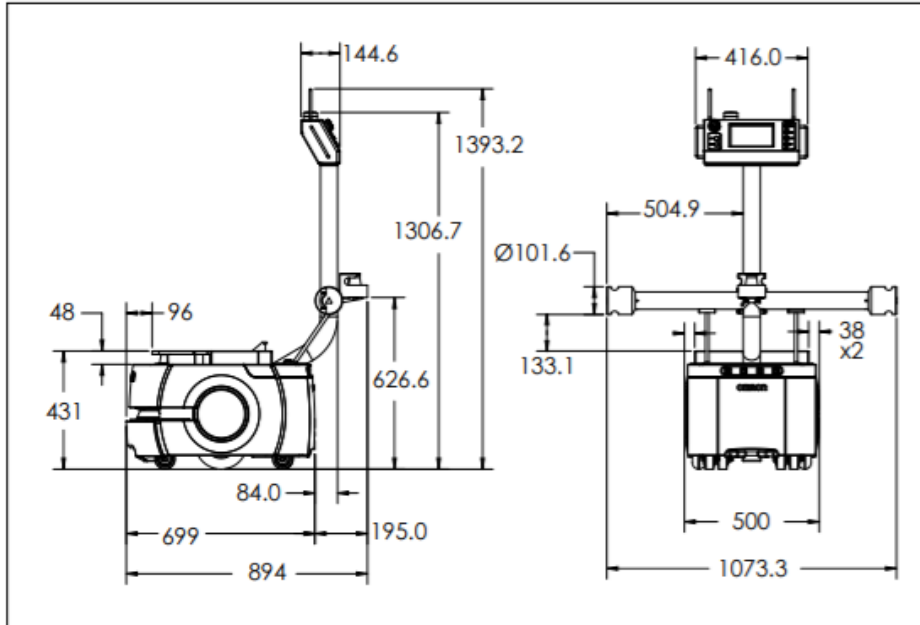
Dimensions du haut, du côté et de l'avant de la plate-forme
